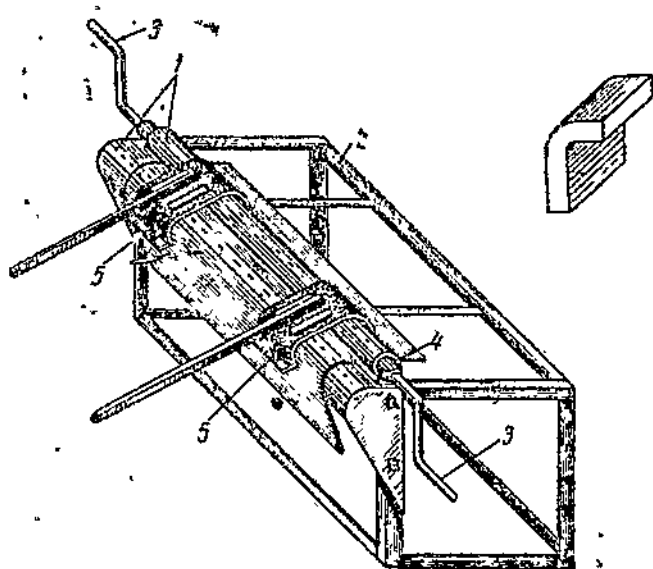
Станок Голубева для изготовления бортовых отсосов.
